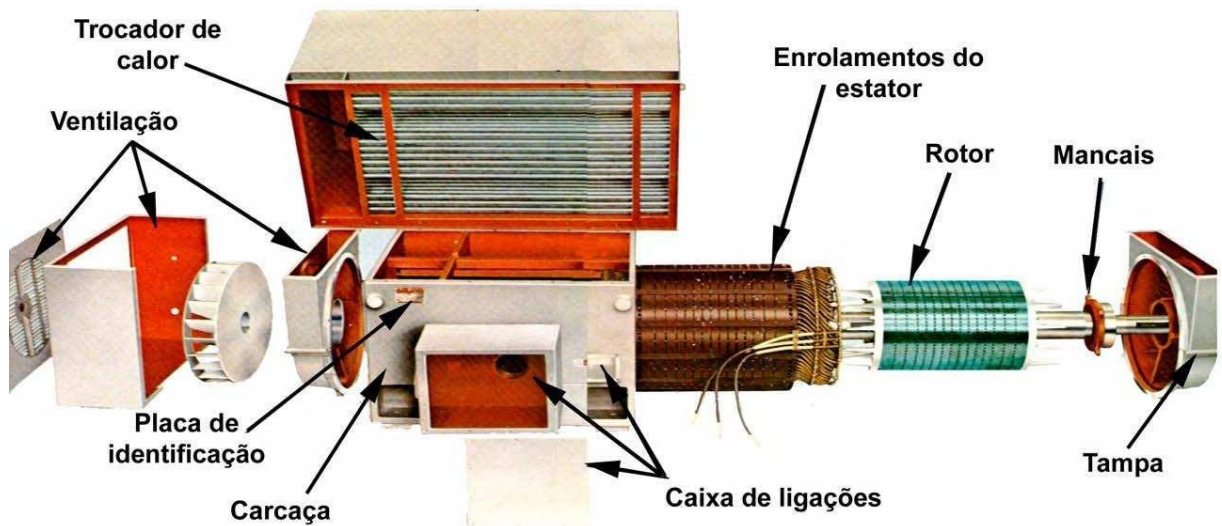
Vista explodida de um motor de indução trifásico. Fonte: ALMEIDA (2004)
